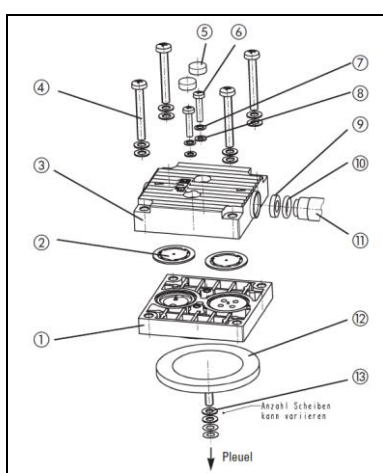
Pumpenkopf (Explosionszeichnung, symbolisch)
